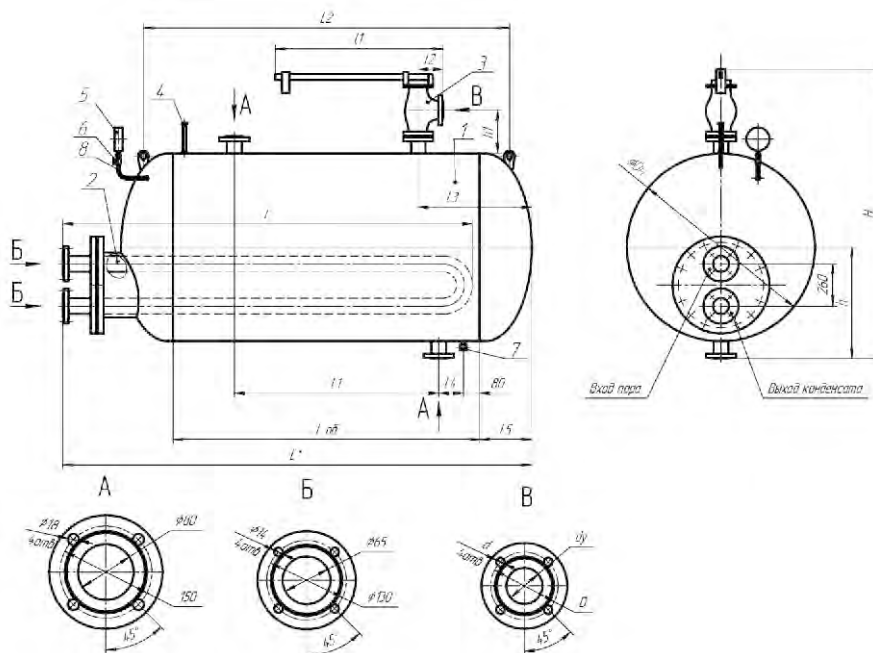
Габаритные и присоединительные размеры водоподогревателей СТД.
